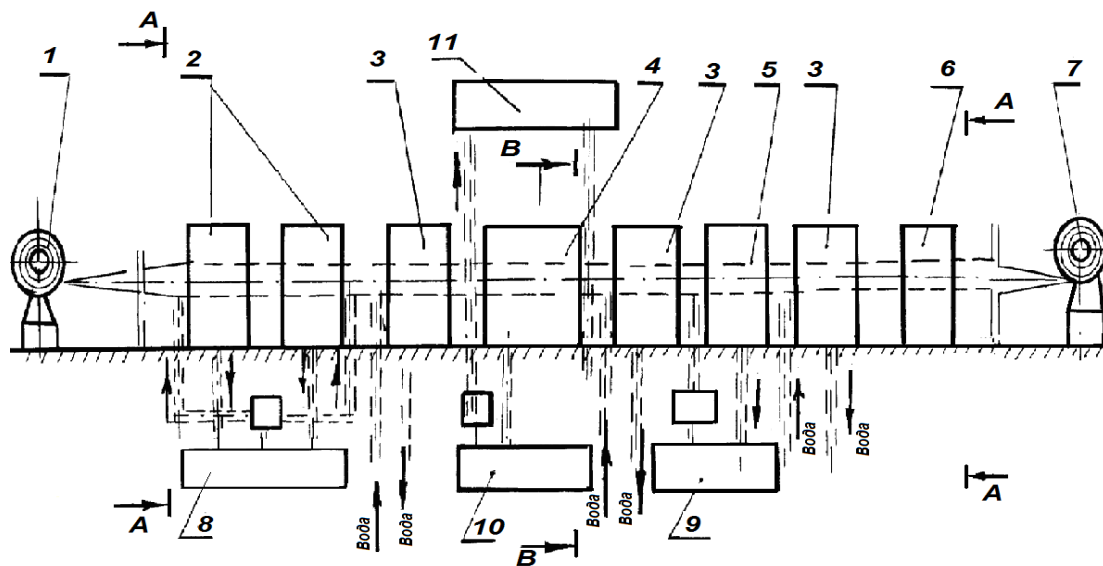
Схема установки для електрохімічного полірування трубчастих елементів зі стрічок
